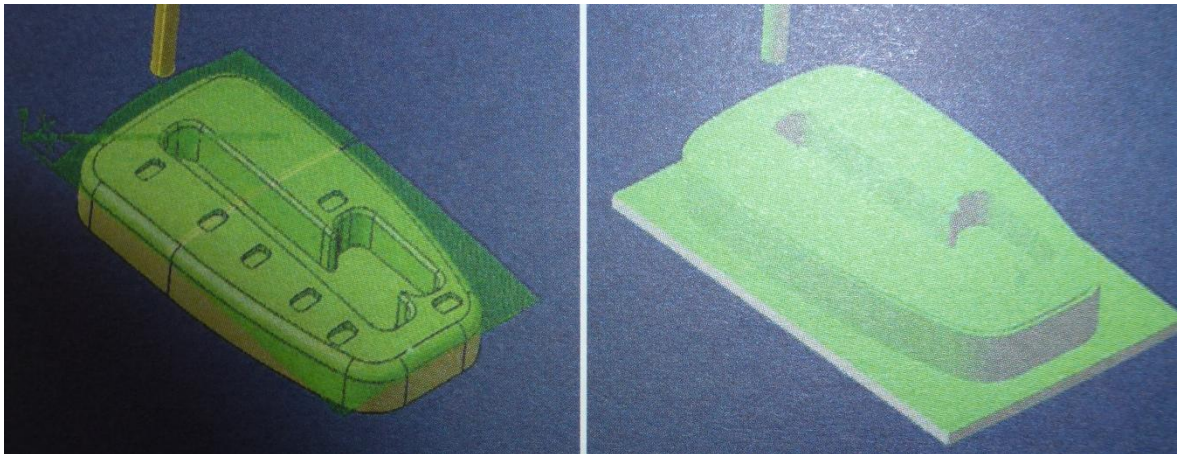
Definování jednotlivých prvků pro obrábění nahrubo a sladění počátku souřadnicového systému CAD/CAM se souřadnicovým systémem stroje [10]
